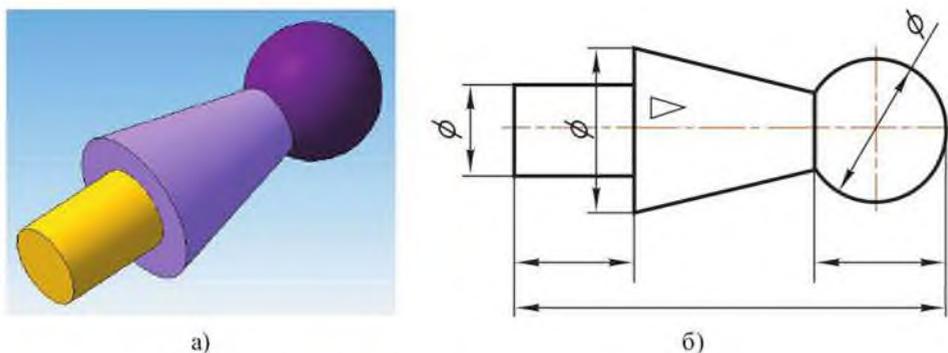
3D-модель (а) и чертёж детали (б)
